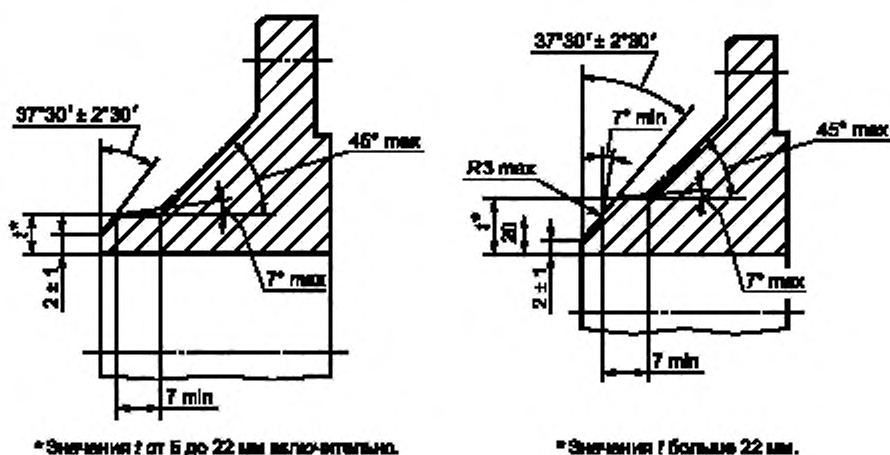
Разделка кромок под сварку для фланцев типа 11, ряд 2
